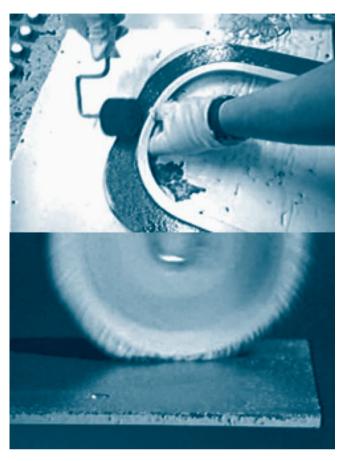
装配前密封涂胶工艺 Fig.2 Seal coating process before assembly
